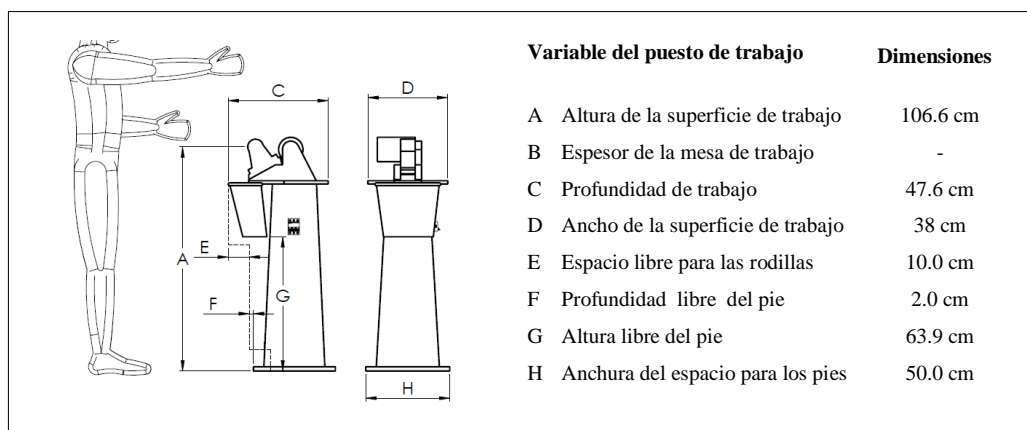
Dimensiones actuales del puesto de refilado de plantillas
